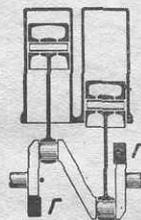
Схема двухцилиндрового двигателя с кривошипами, смещенными на 180° и направленными в разные стороны.
